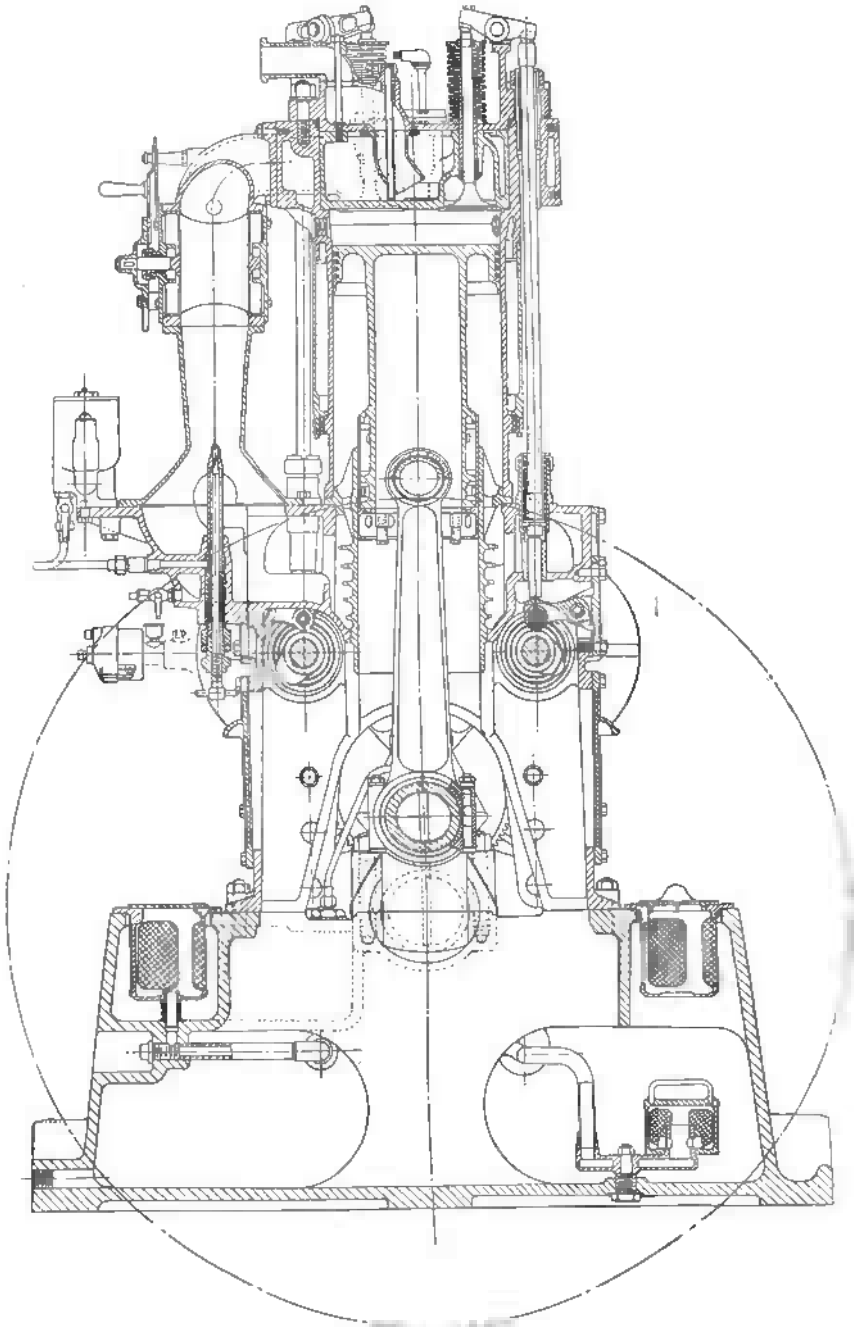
Senkrechter Schnitt durch die Einzylinder-Versuchsmaschine. 209,55 mm
